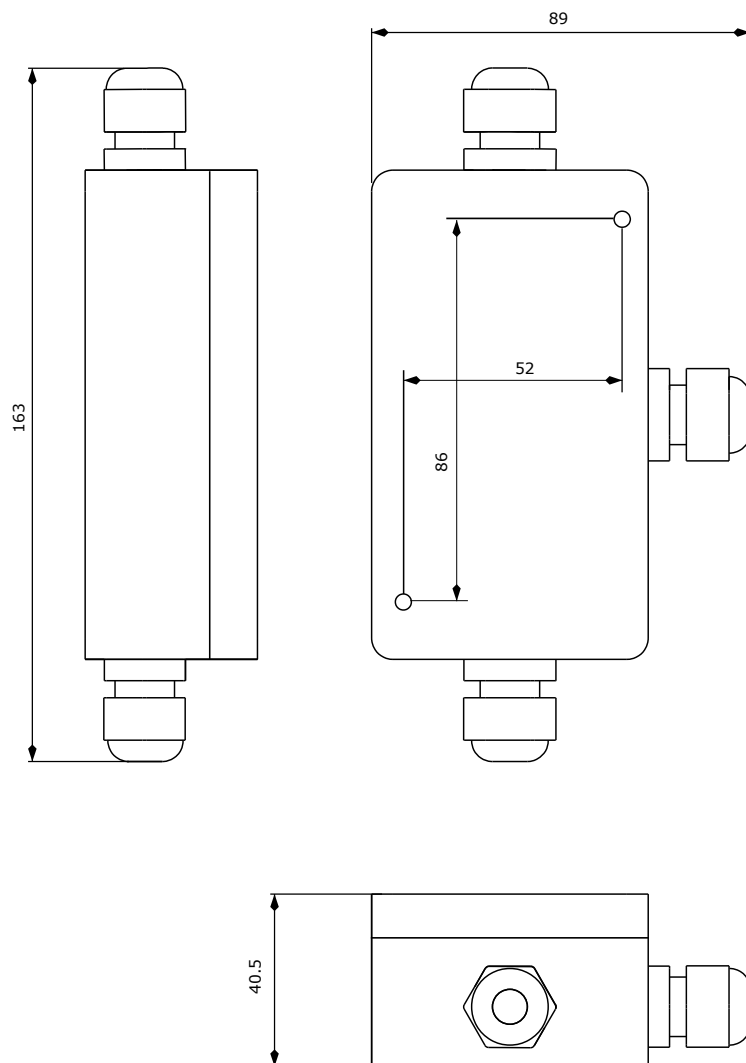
Габаритные и установочные размеры РК-ЗС IP65
